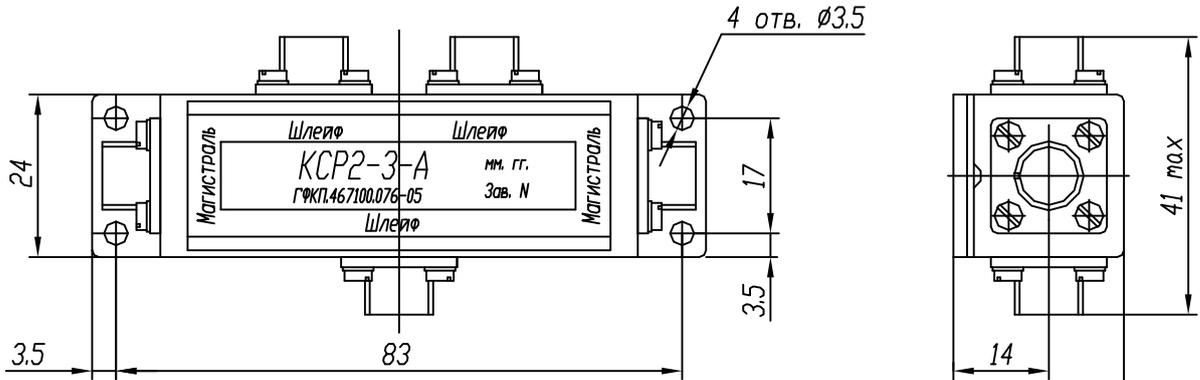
Габаритный чертеж коробки КСП2-3-А
